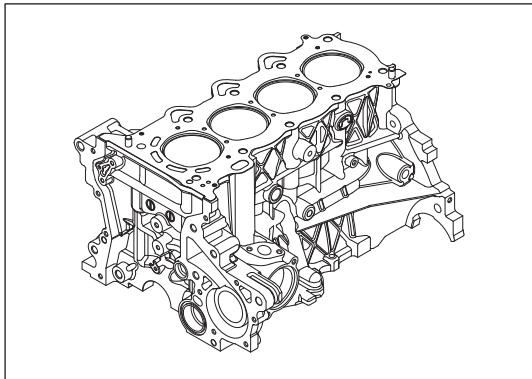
Установка прокладки головки блока цилиндров
